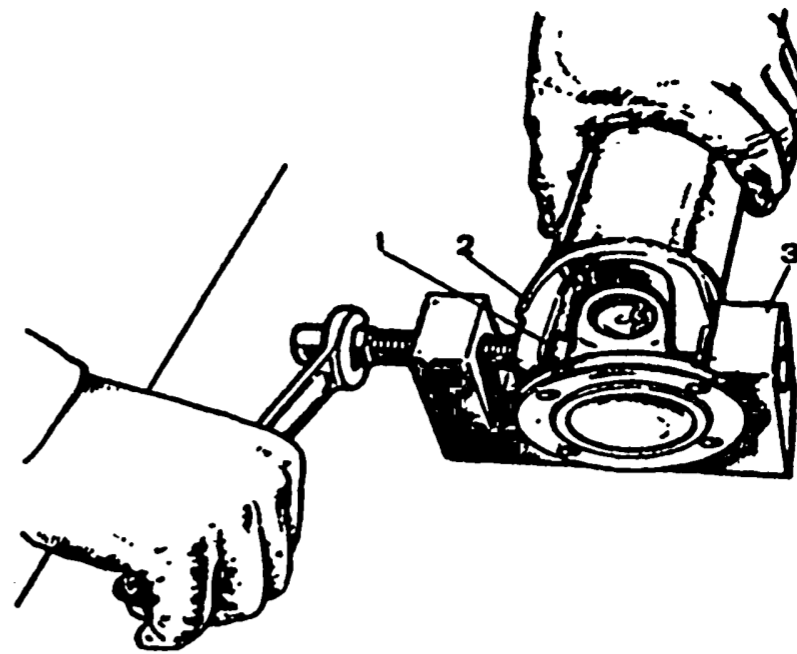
Выпрессовка подшипников крестовины из вилок карданного шарнира: 1 - игольчатый подшипник; 2 - вилка карданного шарнира; 3 - струбцина 67.7823.9522
